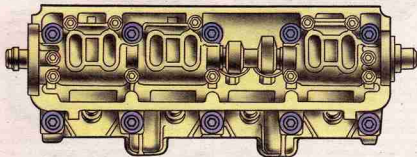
Порядок затягивания болтов головки цилиндров
